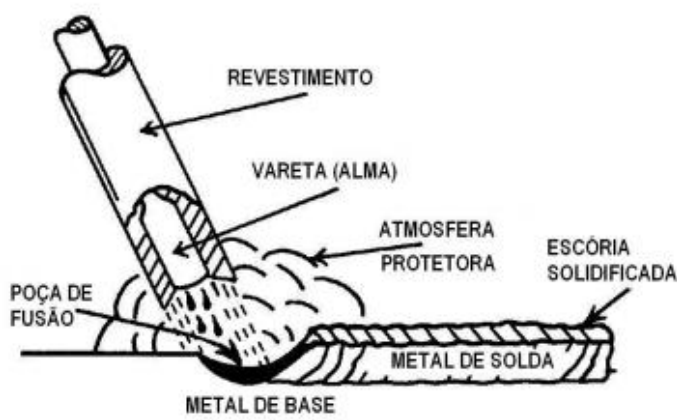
Soldagem a arco elétrico com eletrodo revestido.
